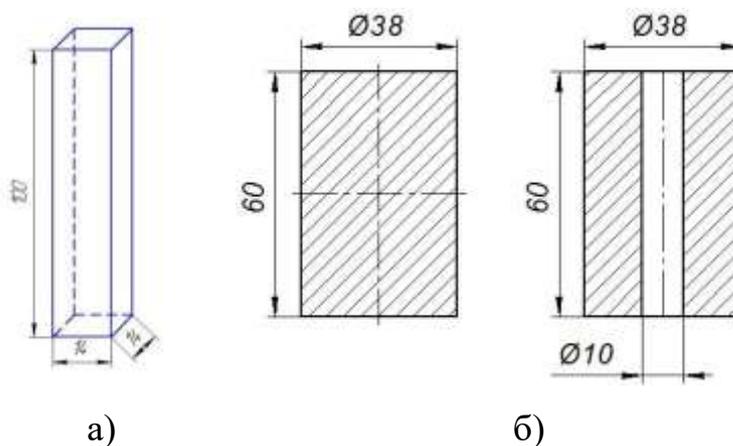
Призматичні (а) та циліндричні (б) заготовки, отримані методом порошкової металургії
